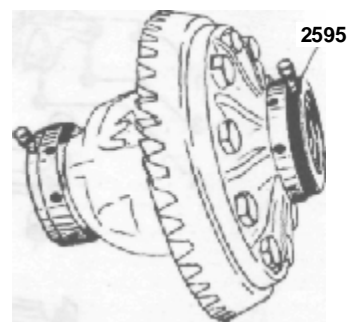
Установка колец подшипников (2595 или аналогичных) на корпусе дифференциала при регулировке зазора и предварительного натяга подшипника дифференциала
